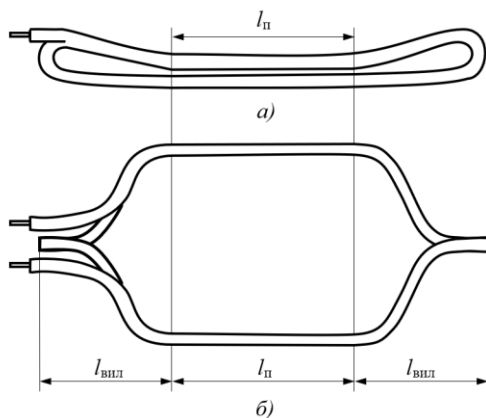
Загальний вид котушки двоярної обмотки статора
